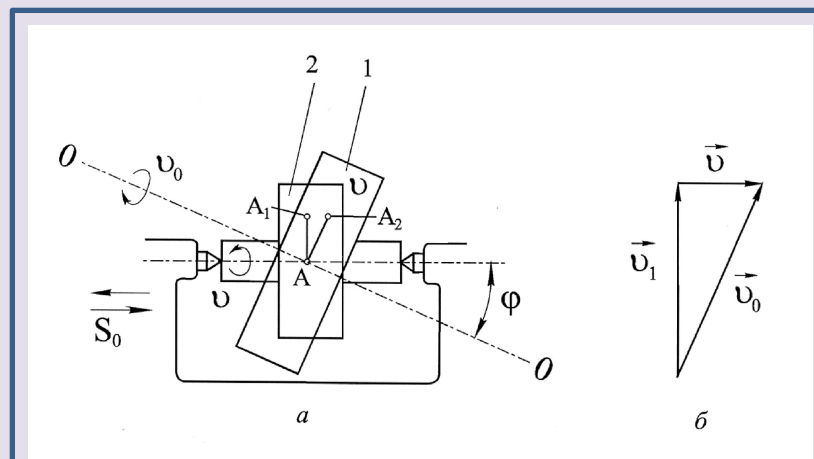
Схема работы дискового шевера (а) и план скоростей при обработке шевером цилиндрических прямозубых колес (б): 1 – шевер; 2 – колесо зубчатое
